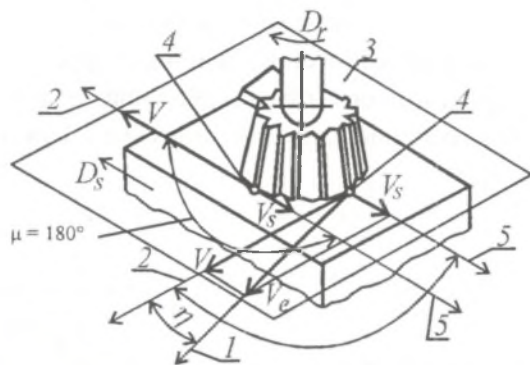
Элементы движений при фрезеровании торцевой фрезой:
